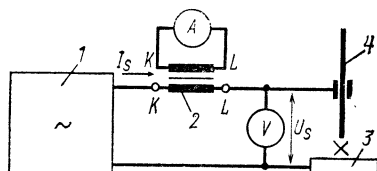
Измерение сварочного тока  $I_s$  и напряжения  $U_s$  при сварке на переменном токе:
